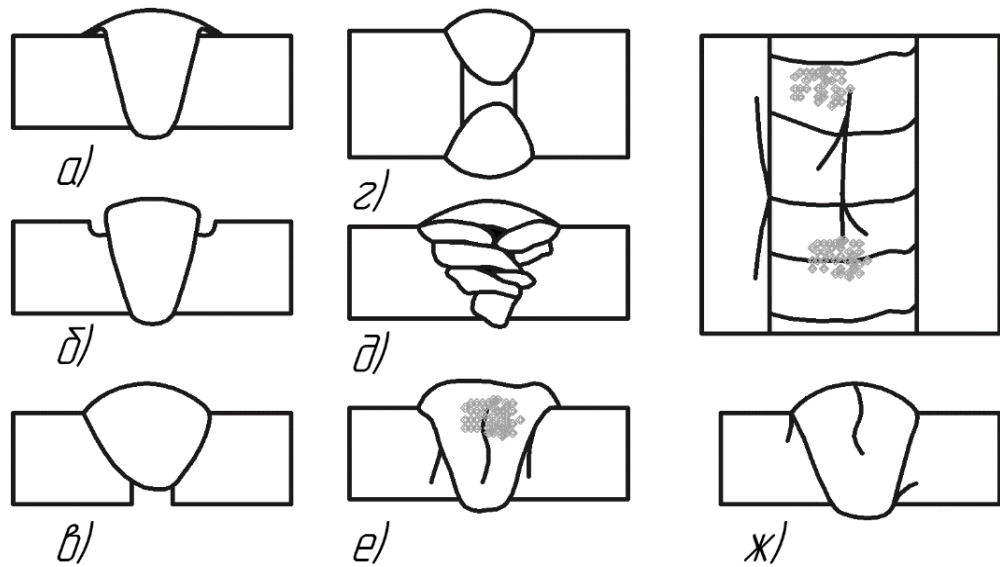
Дефекти зварного з'єднання
